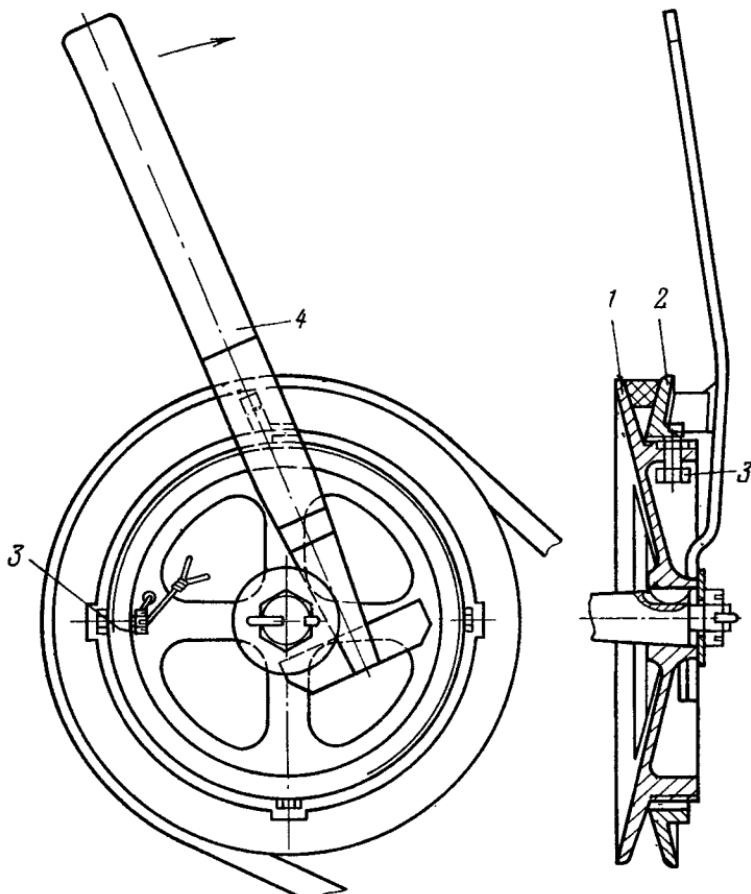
Натяжение ремня резьбовой муфтой шкива компрессора
